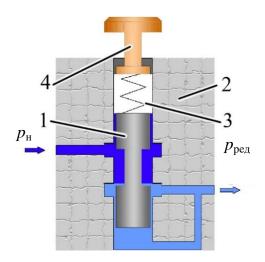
Принципиальная схема редукционного клапана прямого действия: 1 – золотник; 2 – корпус; 3 – пружина; 4 – регулировочный винт
